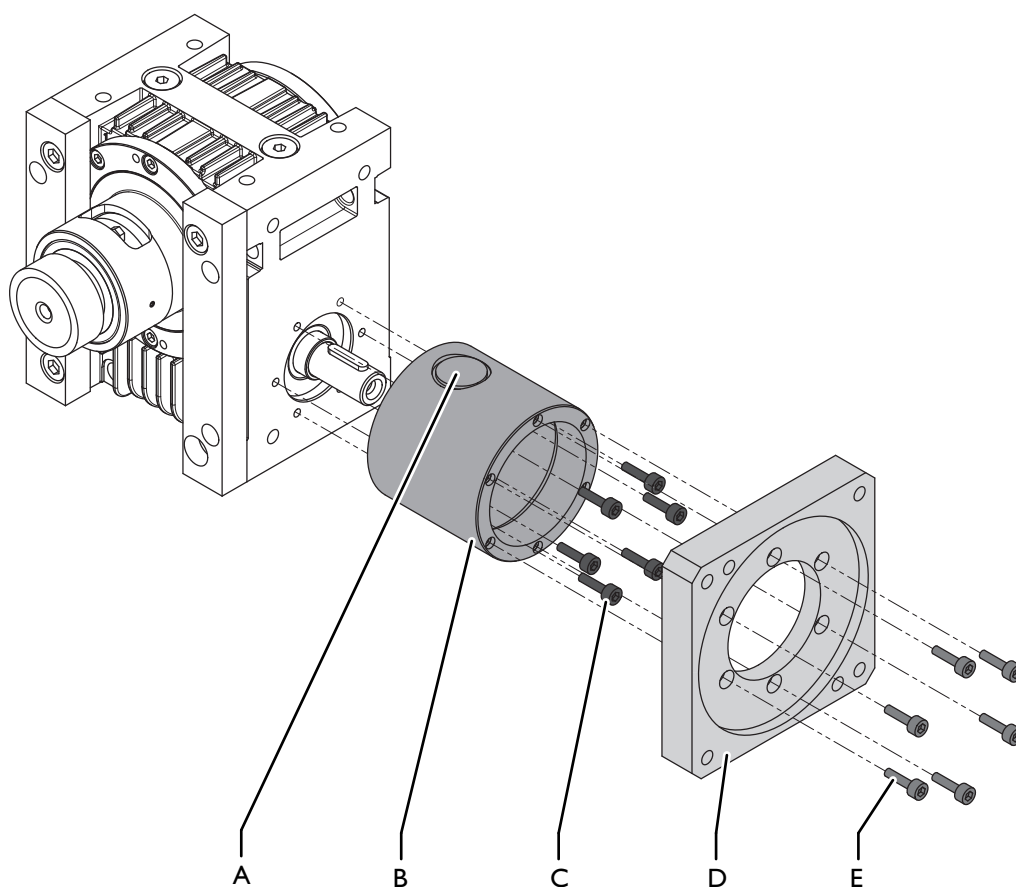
Заменить фланец мотора и фланец редуктора
